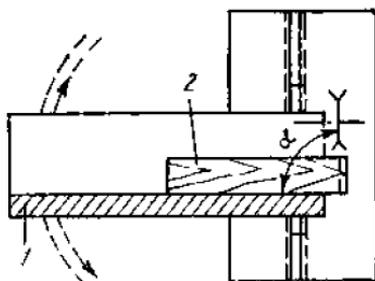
Схема торцевания заготовок на станке с кареткой: 1 — каретка с линейкой; 2 — заготовка
